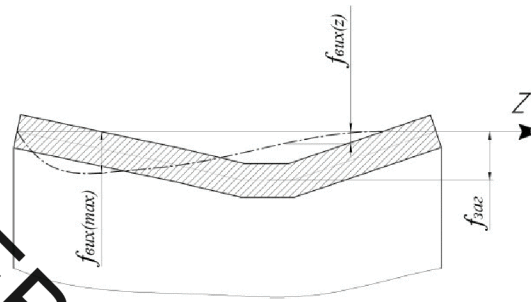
Положення стінки циліндричної заготовки під час повороту вихідної опуклої сторони до індентора
